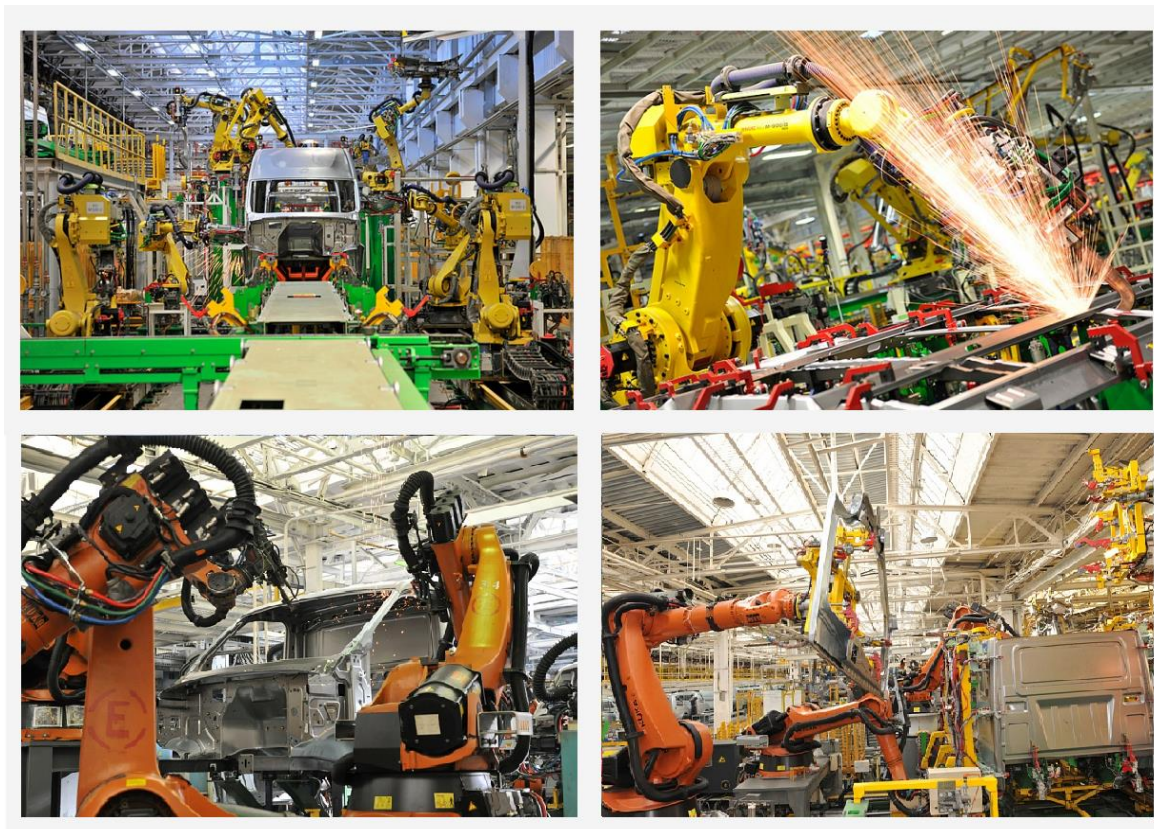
Линия сварки фургонов и линия сварки кабин на заводе ГАЗ
